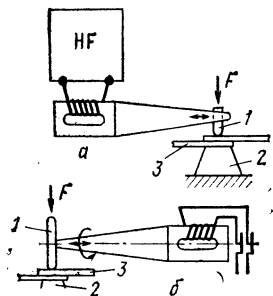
Принцип сварки: а — точечная сварка; б — шовная сварка; 1 — наконечник волновода; 2 — опора; 3 — заготовка
